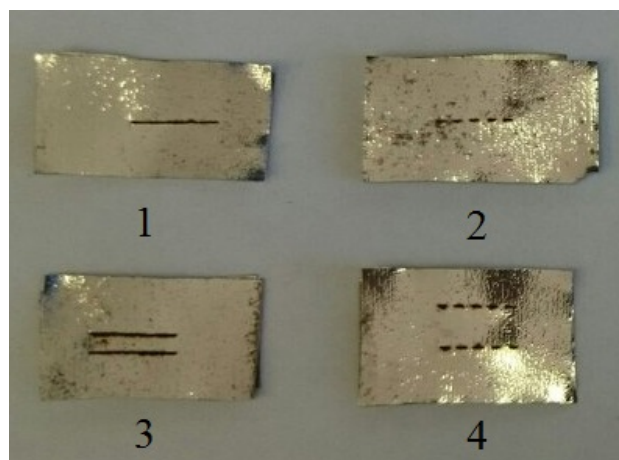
Внешний вид экспериментальных образцов с различными сварными швами: 1 — один сплошной, 2 — один прерывистый, 3 — два сплошных, 4 — два прерывистых
